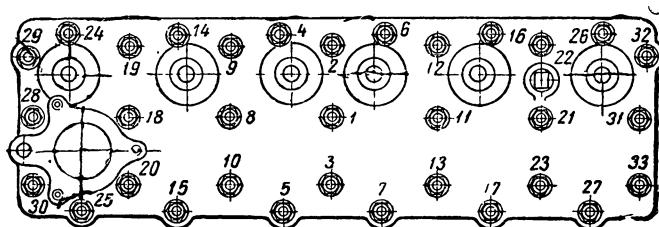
Порядок затяжки гаек шпилек головки цилиндров
